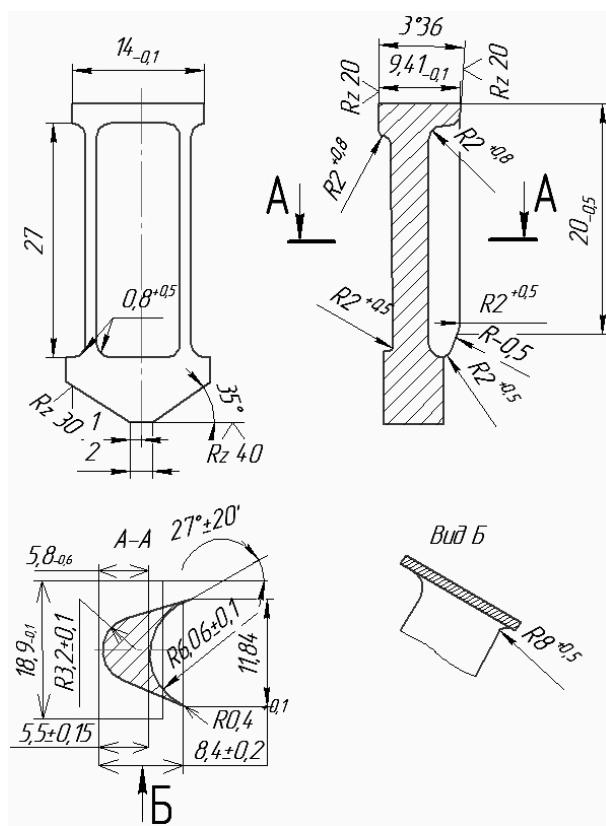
Лопатка турбины ТНА, соединяемая с диском с помощью сварки
